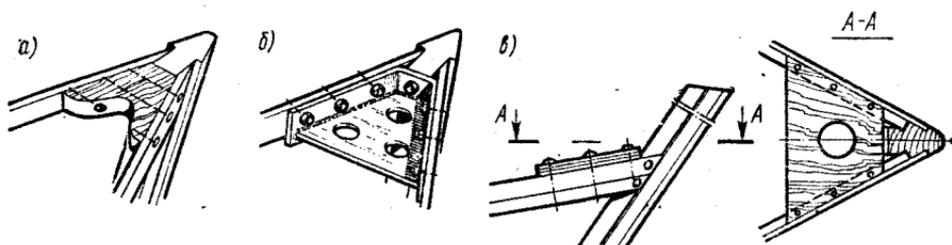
Брежтуки: а — деревянный; б — сварной металлический; в — фанерный
